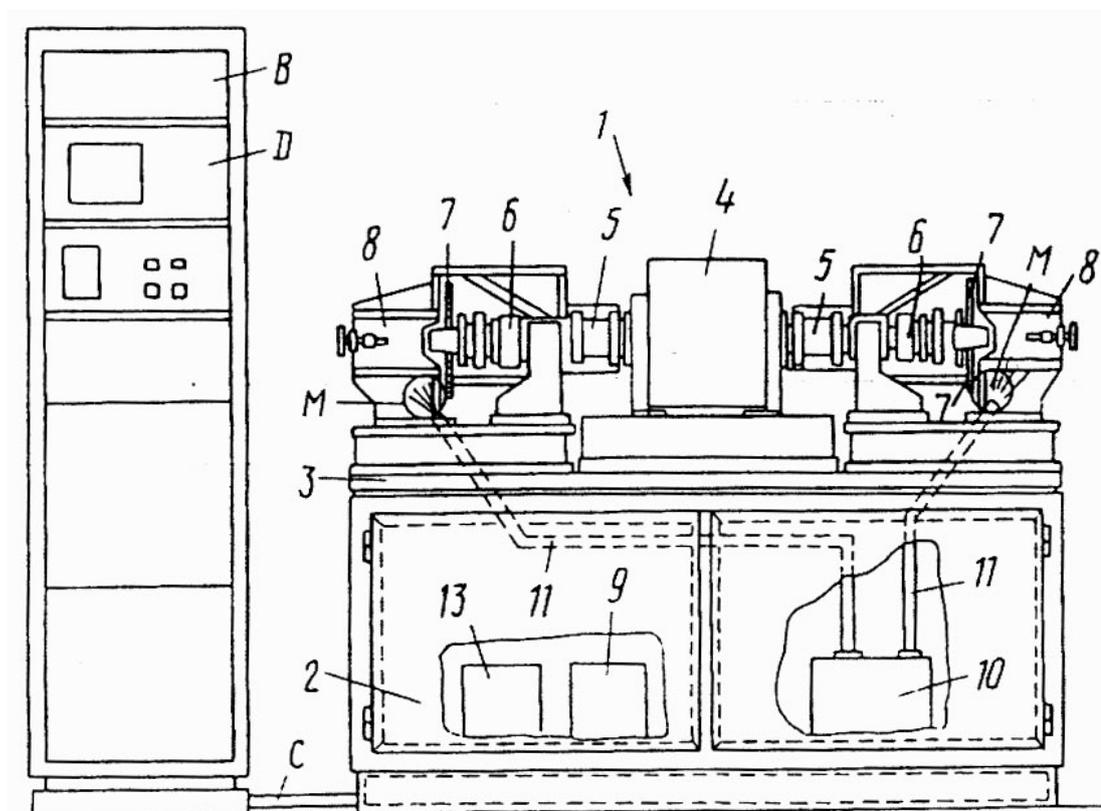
Стенд для испытания стартеров, вид сбоку
